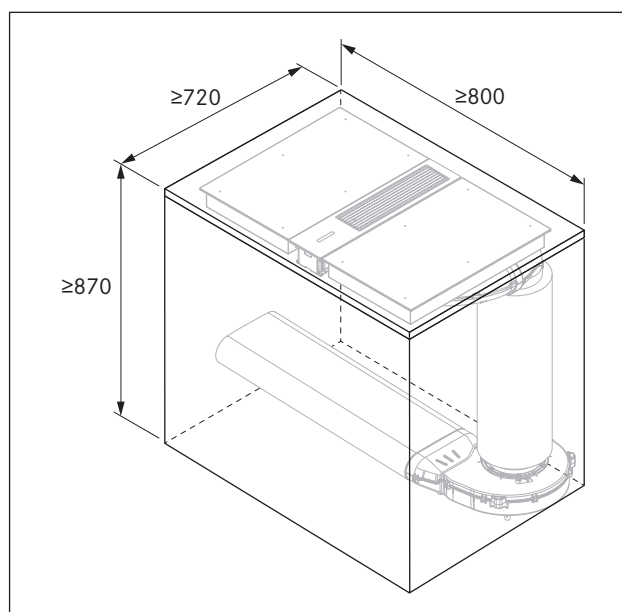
Dimensões mínimas de montagem com silenciador redondo USDR50
